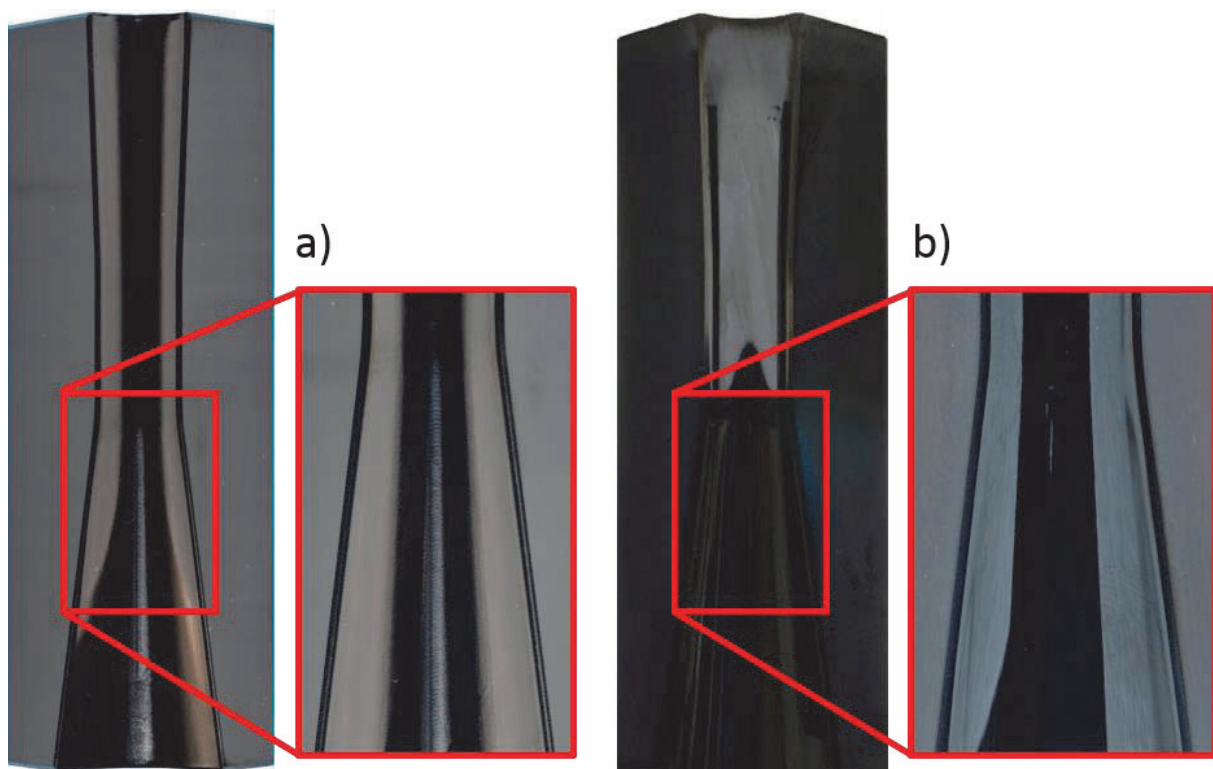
Beschichtete Werkzeuge; a) direkt nach dem Hartfräsen beschichtetes Werkzeug, b) nach dem Hartfräsen poliert und dann beschichtetes Werkzeug.
